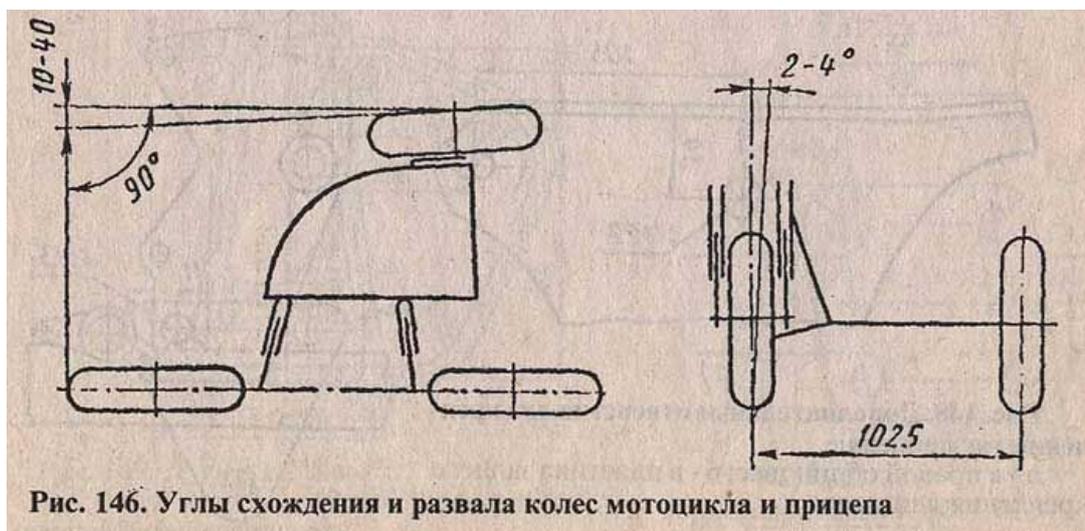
Углы схождения и развала колес мотоцикла и прицепа
